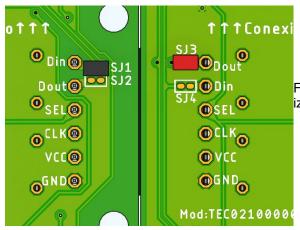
del lado derecho de la imagen el teclado 2 y del lado izquierdo el teclado 1 y los puentes soldados.
